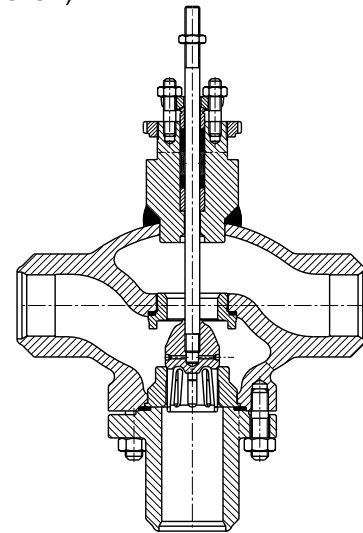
Регулирующий клапан с выводами для сварки
